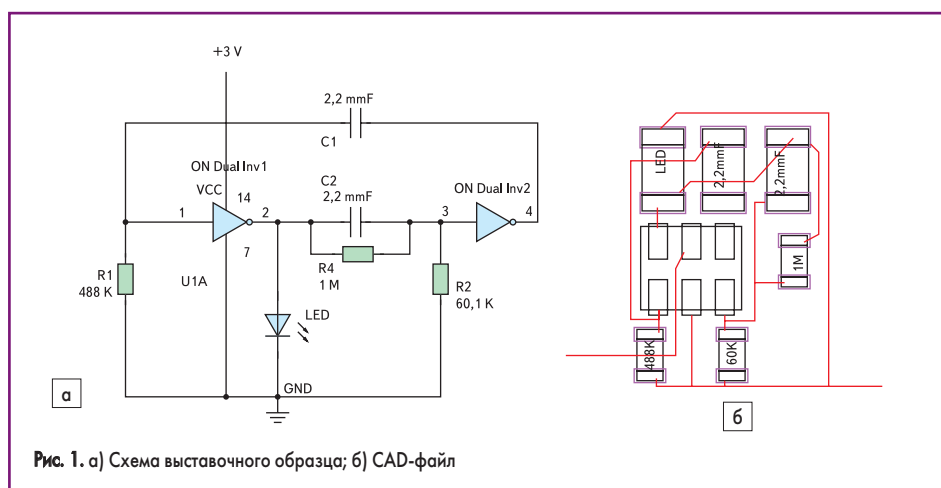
а) Схема выставочного образца; б) CAD-файл
